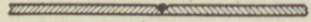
Schweißnaht für Bleche von 3—15 mm Stärke.
